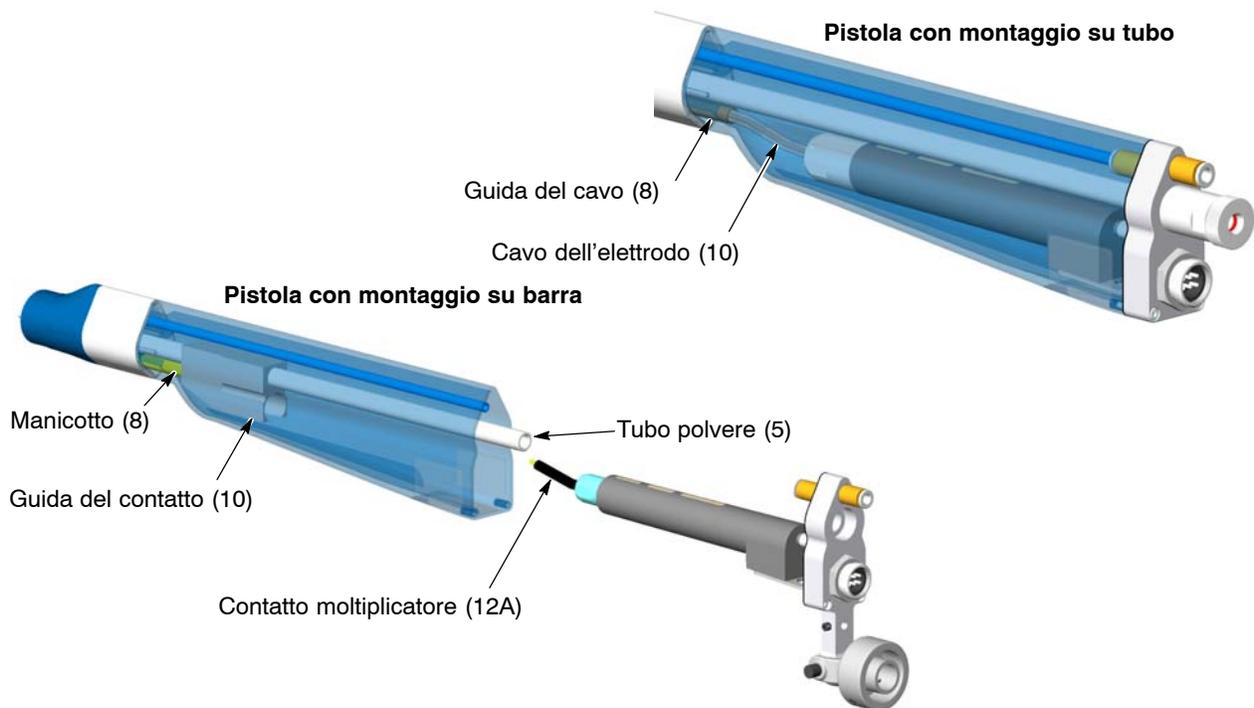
Montaggio del moltiplicatore: Passaggio 6
